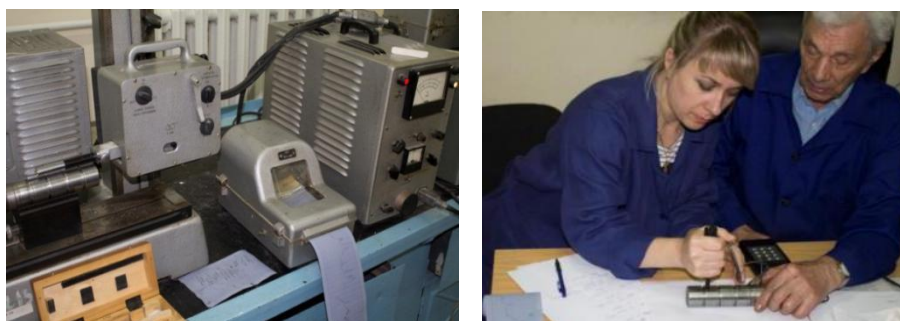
Испытываемый образец детали и инструменты для обкатки
